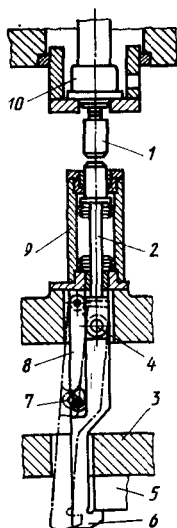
Гидропружинный способ крепления верхнего бойка ковочного пресса
